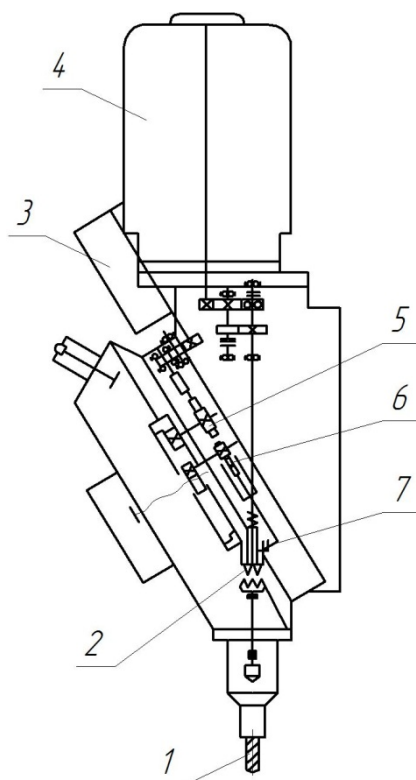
Конструкція привода з револьверною головкою з поворотними шпинделями
